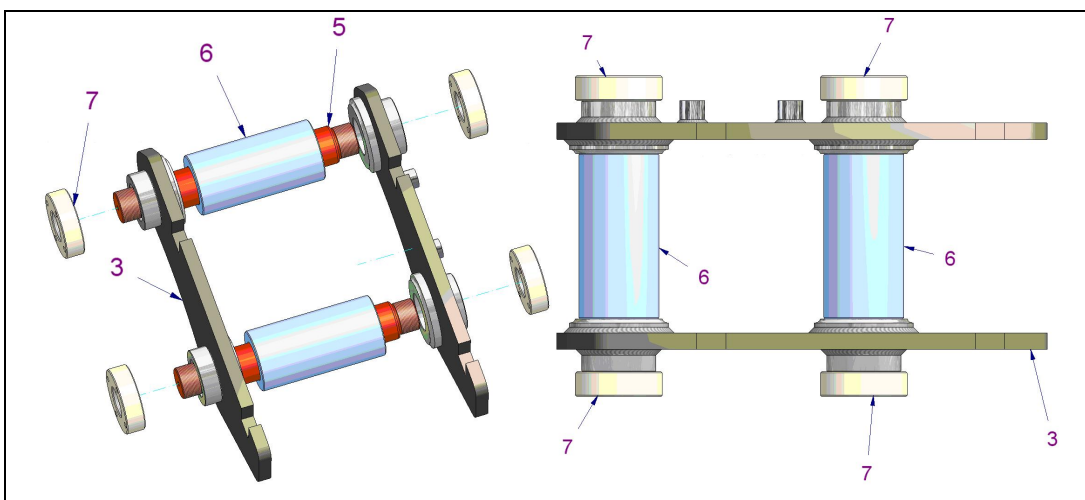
exemple de dispositif de soudage du BVC
